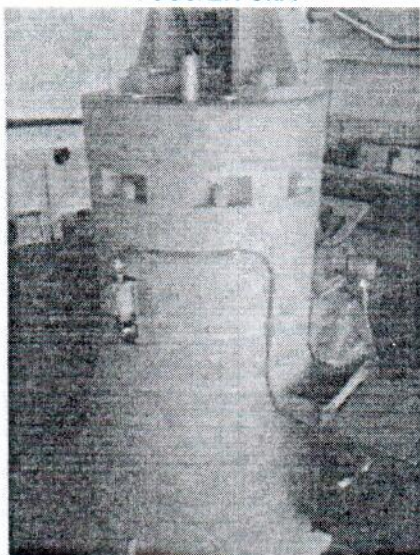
Биозащитный корпус устройства перегрузочного M056A.02.00.000
